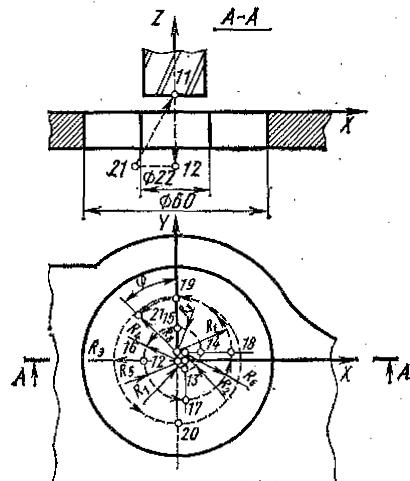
Схема расфрезеровки отверстия диаметром 60 мм детали «крышка»
